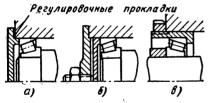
Осевое крепление регулируемых подшипников в корпусах
